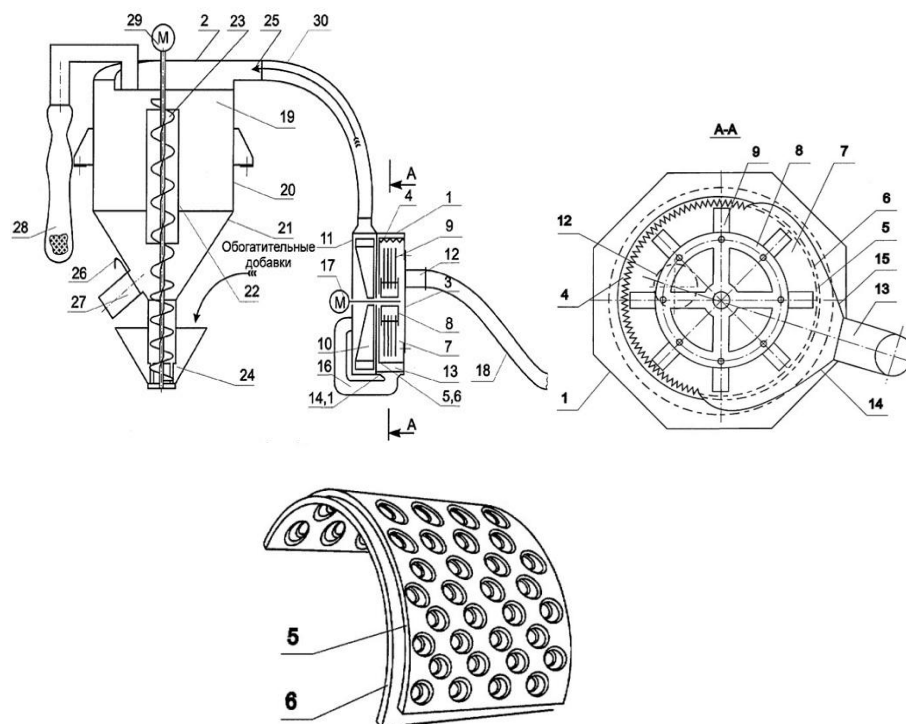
Малогабаритная комбикормовая установка: 1 – дробилка; 2 – бункер-смеситель; 3 – корпус; 4 – деки; 5, 6 – решета; 7 – дробильная камера; 8 – ротор; 9 – молотки; 10 – крыльчатка; 11 – вентилятор; 12 – выгрузочная горловина; 13 – загрузочная; 14, 15 – направляющие; 16 – пневмоканал; 17 – электродвигатель; 18 – шланг загрузки; 19 – смесительная камера; 20 – бункер; 21 – конусное днище; 22 – труба; 23 – шнек; 24 – питатель-дозатор; 25 – загрузочный патрубок; 26 – задвижка; 27 – выгрузочный патрубок; 28 – фильтр; 29 – элетродвигатель; 30 – пневмопровод
